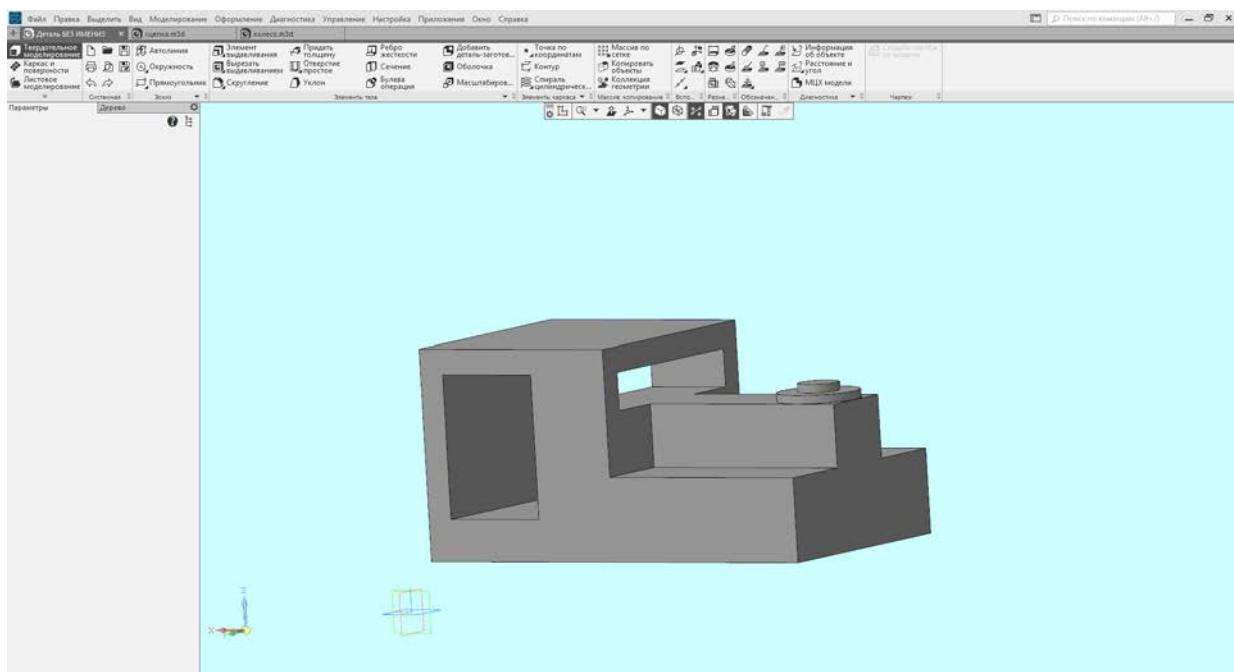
Промежуточный внешний вид детали после завершения операции «Вырезать выдавливанием»
